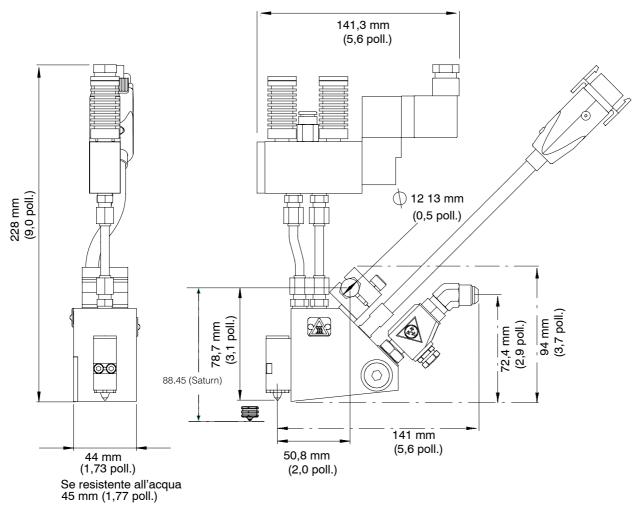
Dimensioni di una pistola configurabile a modulo singolo con elettrovalvola SG
